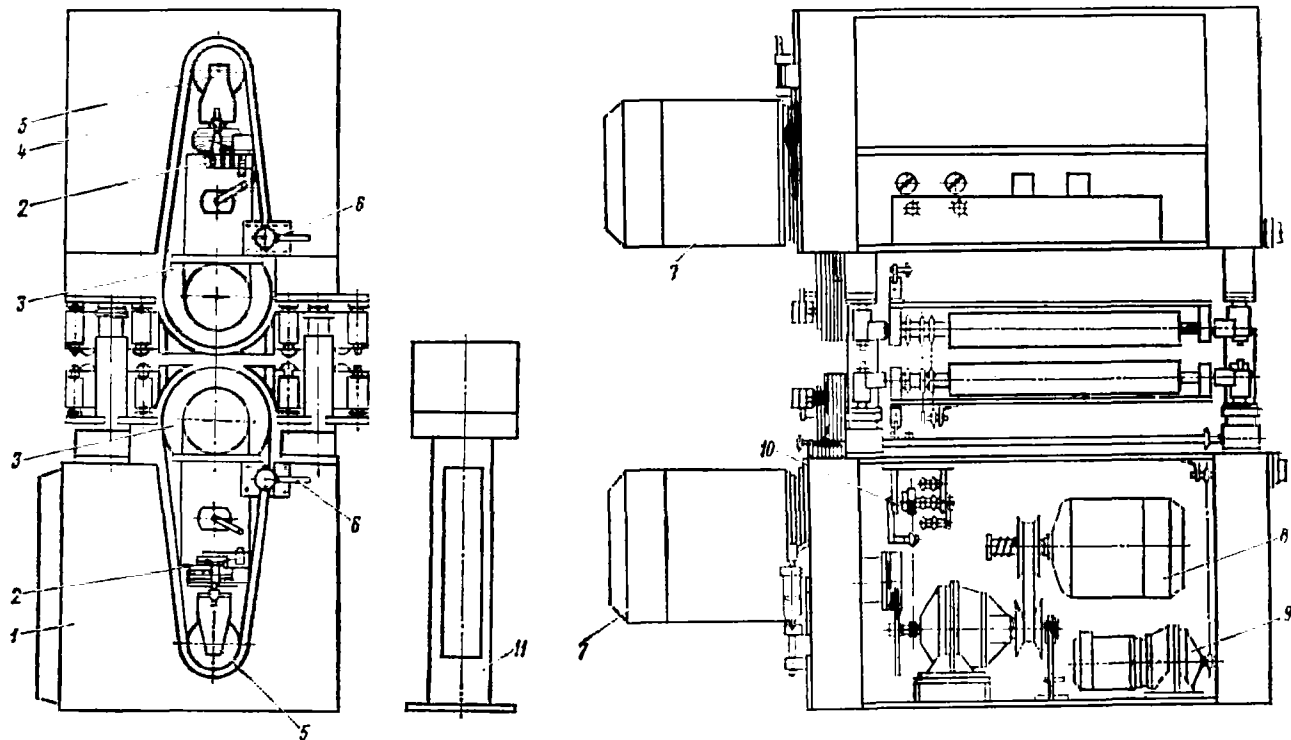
Схема калибровально-шлифовального станка МКШ-01:
